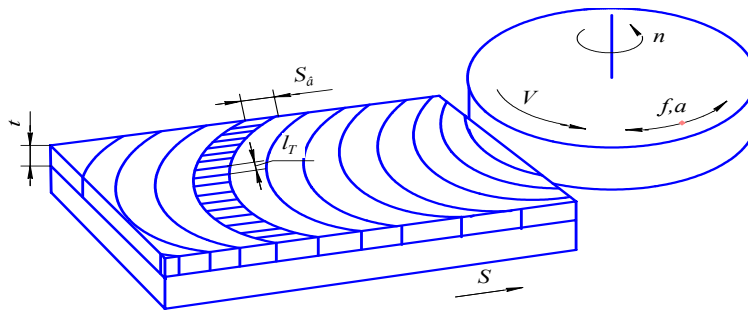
Схема способа обработки плоских поверхностей вибрационным резанием
